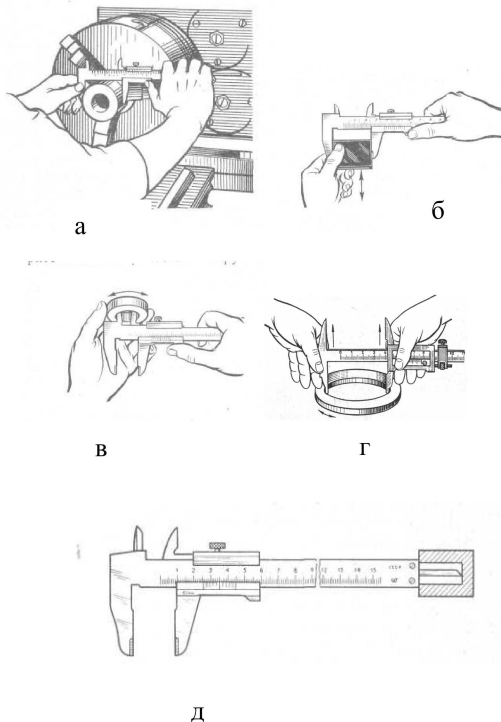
Техника измерения размеров деталей штангенциркулем: а – закрепленной детали в патроне станка; б – незакрепленной детали; в и г – внутренних размеров изделий; д – глубины глухих отверстий.
